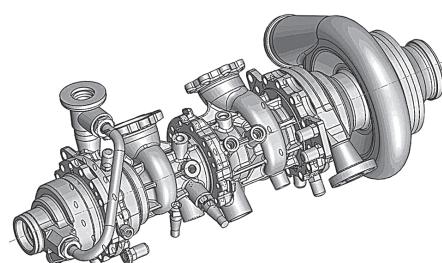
Внешний вид ТНА двигателя 11Д58МФ
